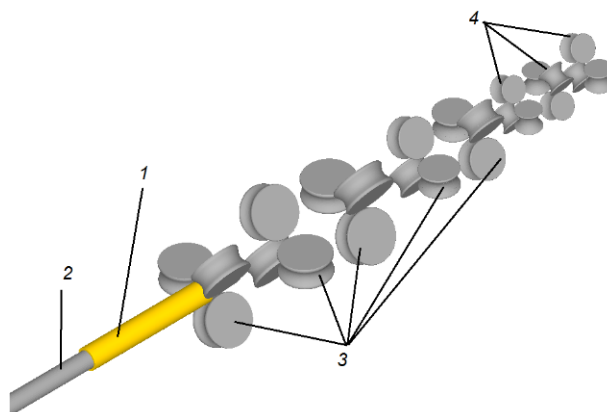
Твёрдотельная модель непрерывного стана FQM со станом-извлекателем: 1 – заготовка; 2 – оправка; 3 – валки стана FQM; 4 – валки стана-извлекателя
